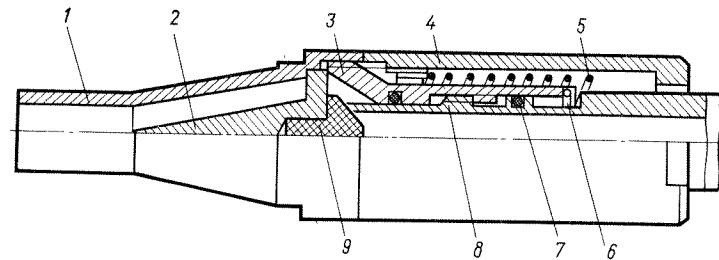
Пожарный ствол: 1 — насадок; 2 — обтекатель; 3 — корпус; 4 — стакан; 5 — пружина; 6 — стопорное кольцо; 7 — резиновое кольцо; 8 — шток; 9 — клапан
